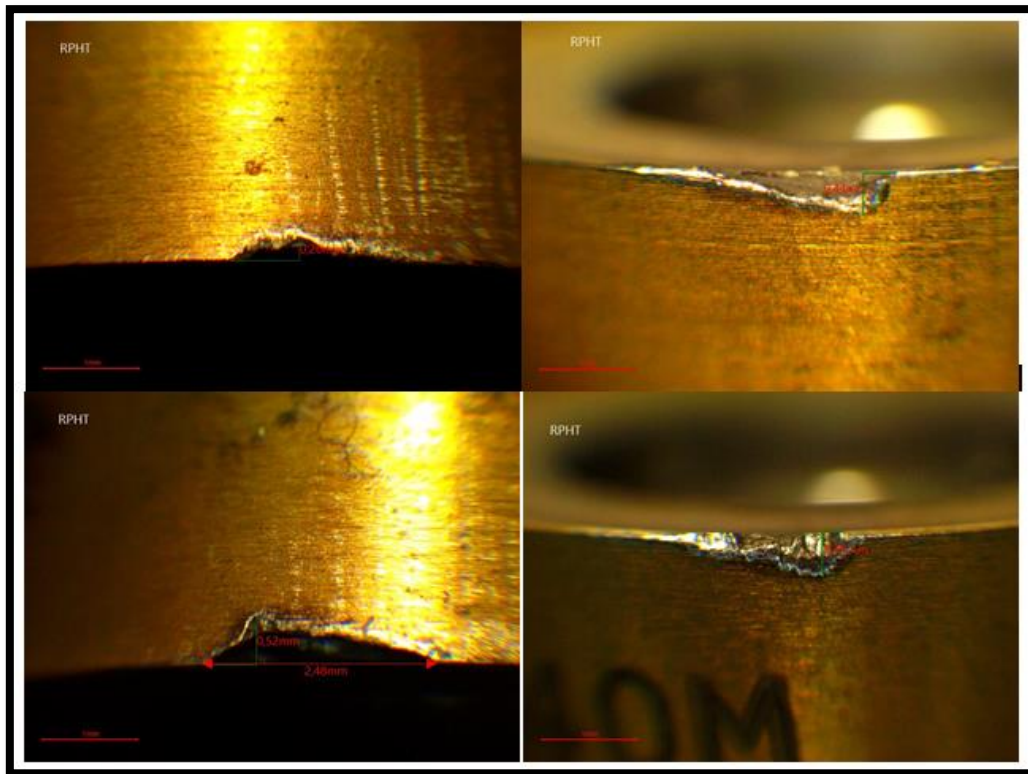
Observation microscopique de l'usure en dépouille fracture sur les faces de dépouille des plaquettes type RPHT revêtue.
